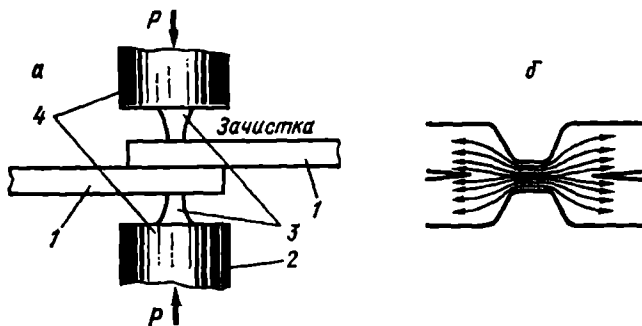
Схема процесса точечной холодной сварки (а) и разрез сварной точки (б):
